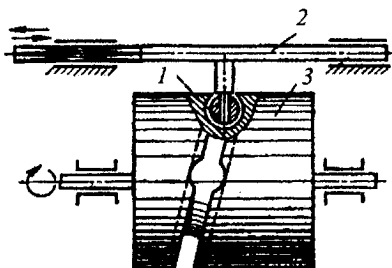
Кулачковий механізм з канавкою тороподібної форми
